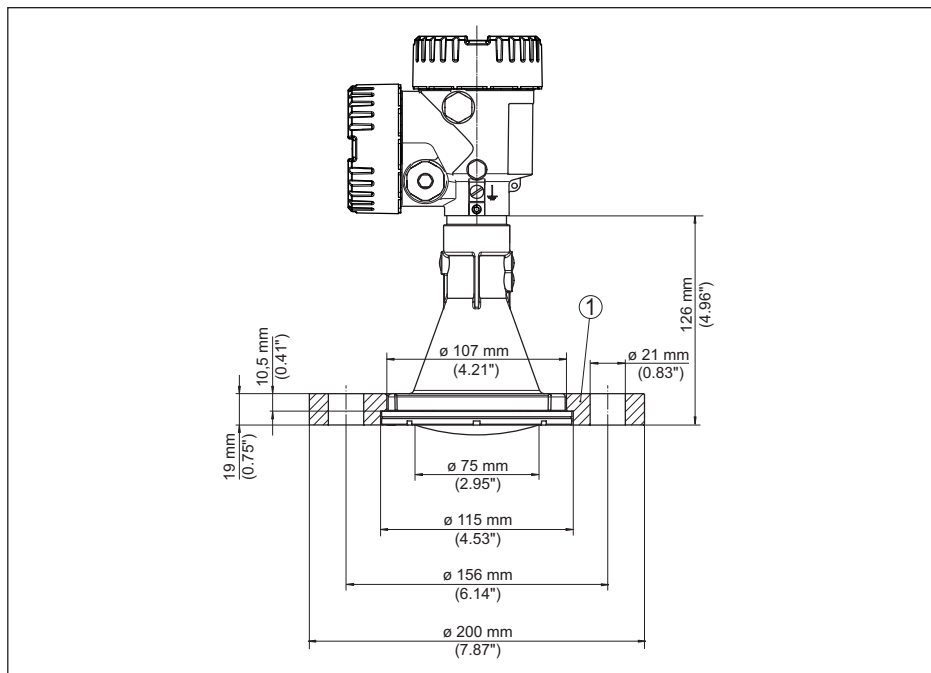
NCR-86 com flange de capa adequado para 3" 150 lbs, DN 80 PN 16
